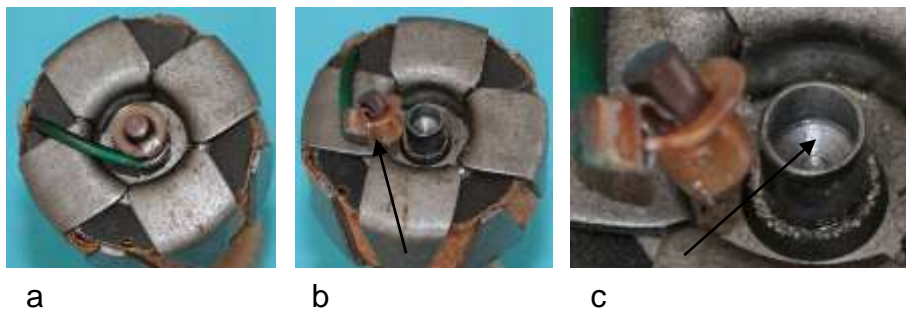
Spannung führender Schleifkontakt: a) Spulenanschluss, b) Isoliert eingebaute Kupferbürste, c) Grundbohrung in der Welle
